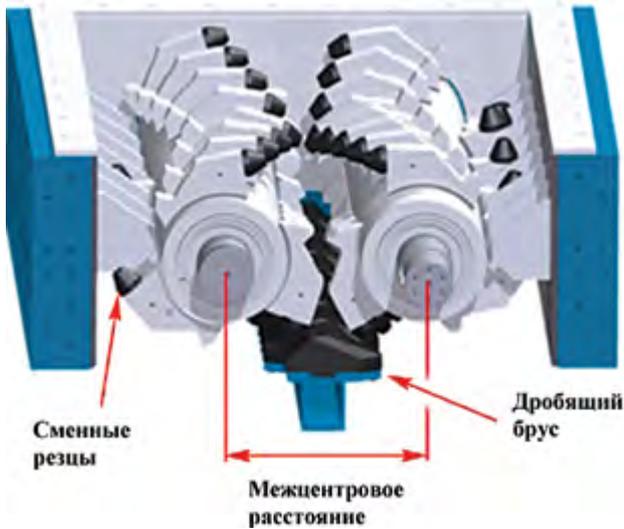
Дробильные инструменты конструкции центрального дробления CenterSizer
